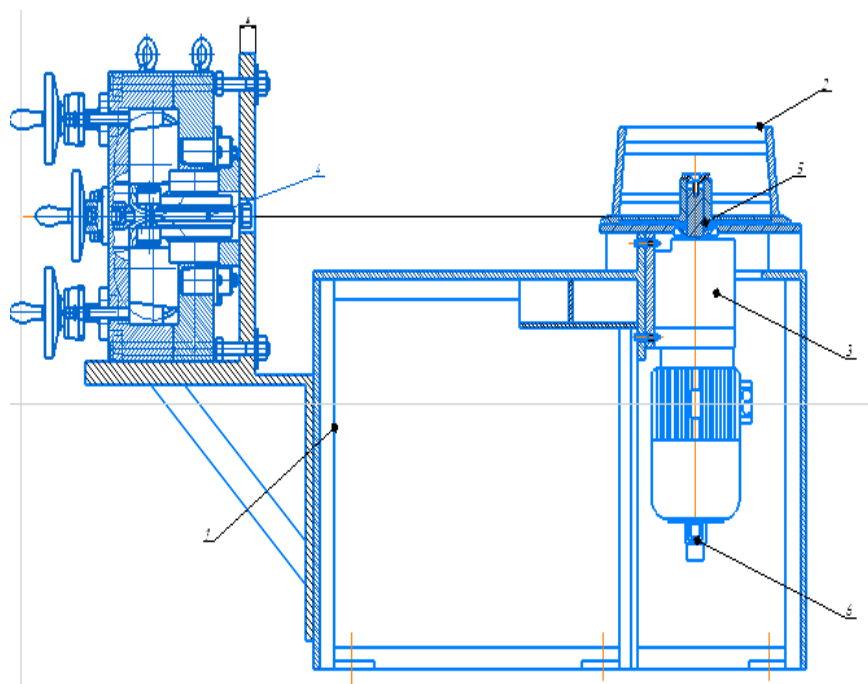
Блок волочильный. 1 – Рама; 2 – Тянущий барабан; 3 – Соосный цилиндрический моторредуктор; 4 – Роликовая волока; 5 – Упорный подшипник; 6 – Узел энкодера.
